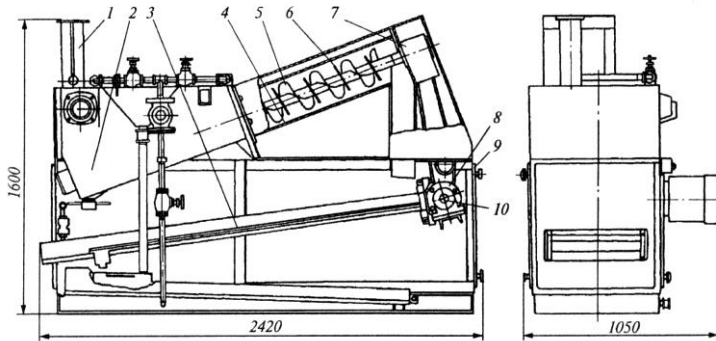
Шнекова мийна машина А1 – БГМ: 1 – живильник; 2 – мийна ванна; 3 – ситовий кузов; 4 – корпус; 5 – шнек; 6 – лопатки; 7 – черв'ячний редуктор; 8 – електродвигун; 9 – станина; 10 – ексцентрикний коливач
